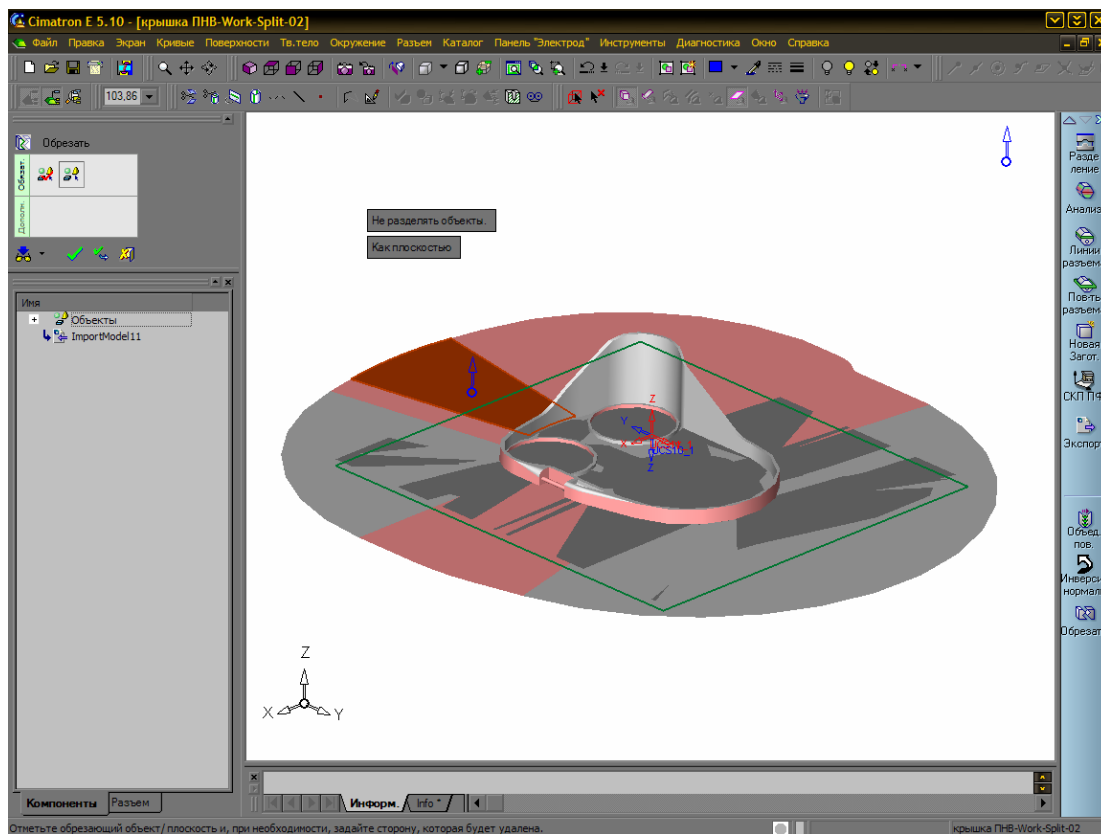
Окончание обрезки заготовки матрицы
